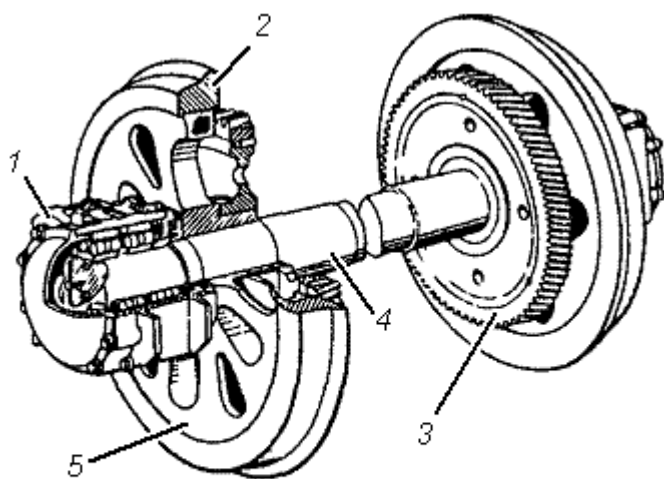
Колесная пара электровоза: 1 – корпус буксы; 2 – бандаж; 3 – зубчатое колесо; 4 – ось; 5 – колесный центр
